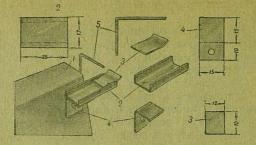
Направляющий желобок: I — конец стойки, 2 — направляющий желобок, 3 —козырек, 4 — угольник, 5 —ограничивающая шпилька для регулировки пишущего устройства.
